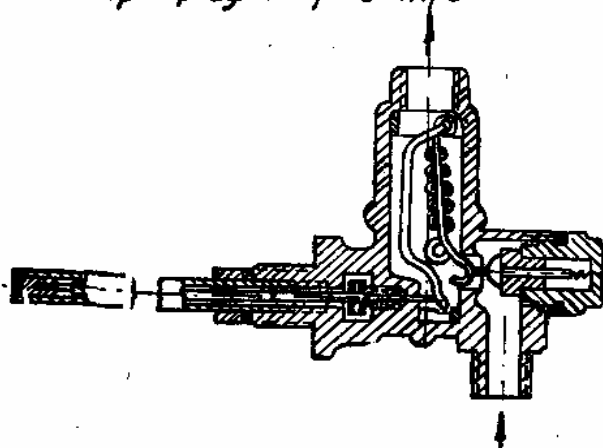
Схема работы терморегулятора: 1—перекидной рычаг; 2—пружина клапана; 3—стакан; 4—прокладка; 5 — втулка клапана; 6—клапан; 7—седло клапана; 8—инваровый стержень; 9—втулка; 10—трубка; 11—гайка; 12—прокладка; 13—пружина; 14—шайба; 15—уплотнительное кольцо; 16—корпус; 17—фигурный рычаг; 18—перекидная пружина.
